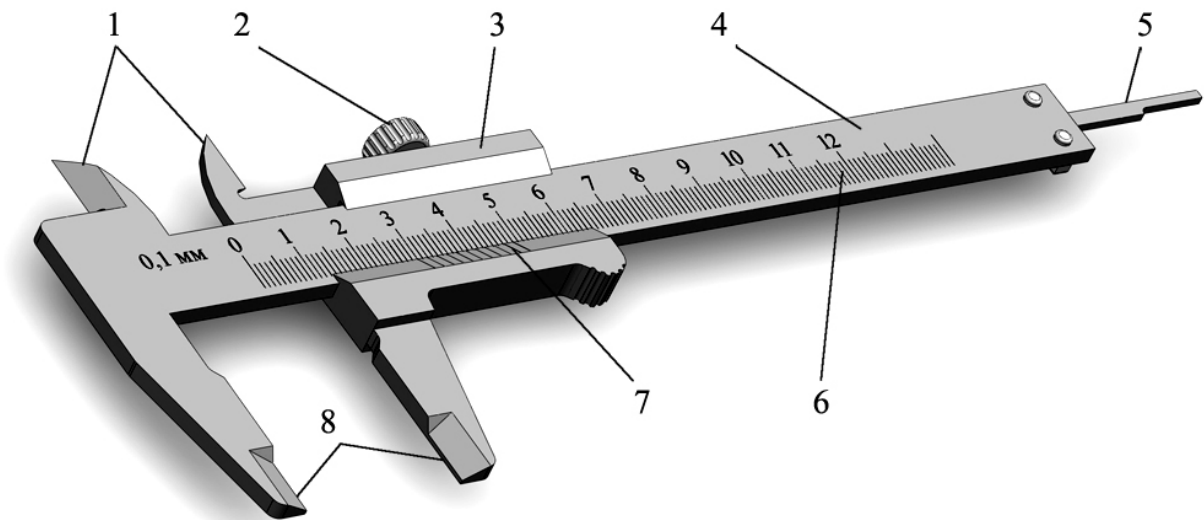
Штангенциркуль ШЦ-I: 1 – губки для внутренних измерений; 2 – зажим рамки; 3 – рамка; 4 – штанга; 5 – линейка глубиномера; 6 – шкала штанги; 7 – нониус; 8 – губки для наружных измерений
